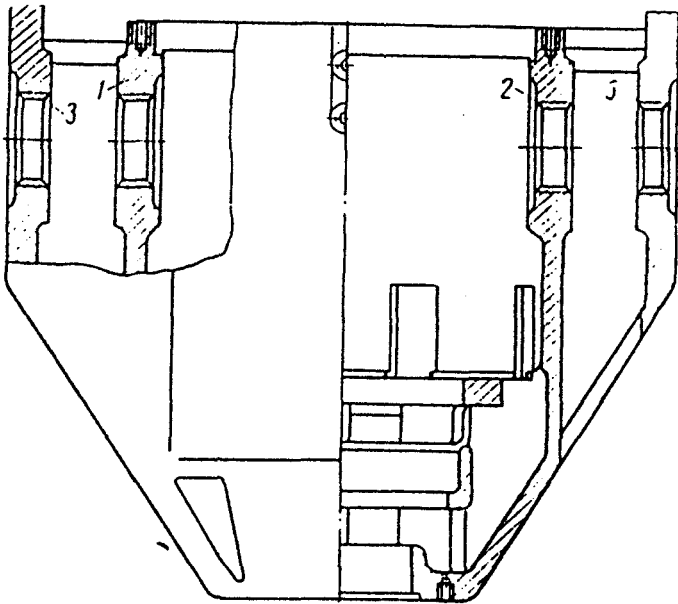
Ремонт корпуса вертлюга способом дополнительных деталей:
